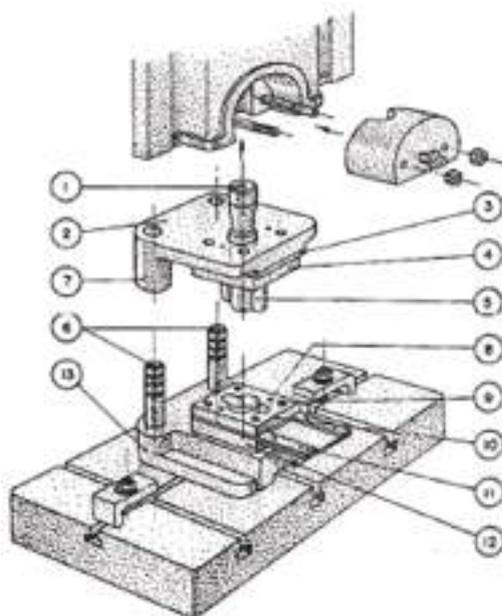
Corte em prensa: 1 – Espiga ou nariz; 2 – Cabeçote ou base superior; 3 – Placa de choque; 4 – Porta-punção; 5 – Punção; 6 – Colunas de guia ou cavilhas; 7 – Buchas ou casquilhos; 8 – Pinos de fixação; 9 – Parafusos de fixação; 10 – Extrator ou placa de guia; 11 – Guias da chapa ou calços de guia; 12 – Matriz; 13 – Base inferior ou bloco inferior; 14 – Mesa da prensa; 15 – Mordaça de aperto do nariz ou dedo de aperto; 16 – Corrediça da prensa.
